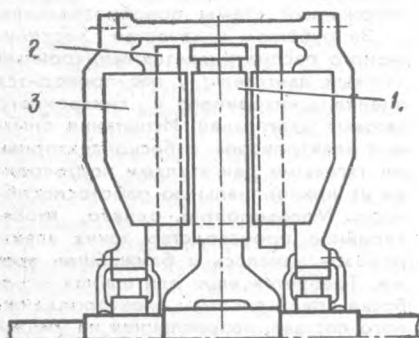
Эскиз тягового двигателя дисковой конструкции
